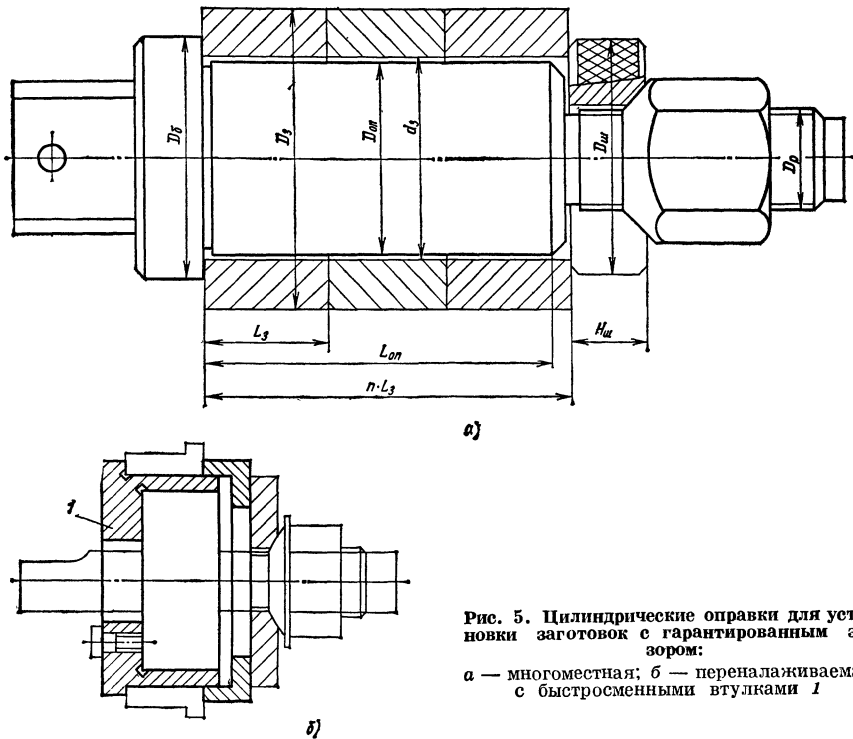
Цилиндрические оправки для установки заготовок с гарантированным зазором:
